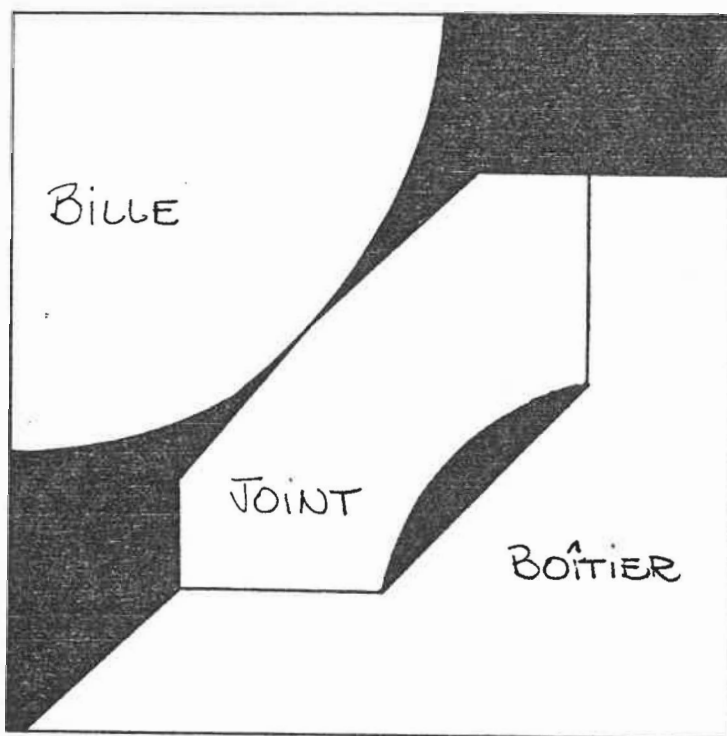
Coupe transversale d'un joint d'étanchéité
